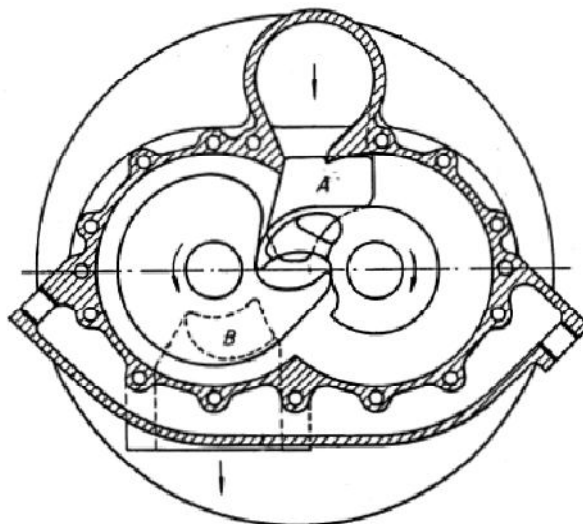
vue en coupe d'un compresseur rotatif à lobes
